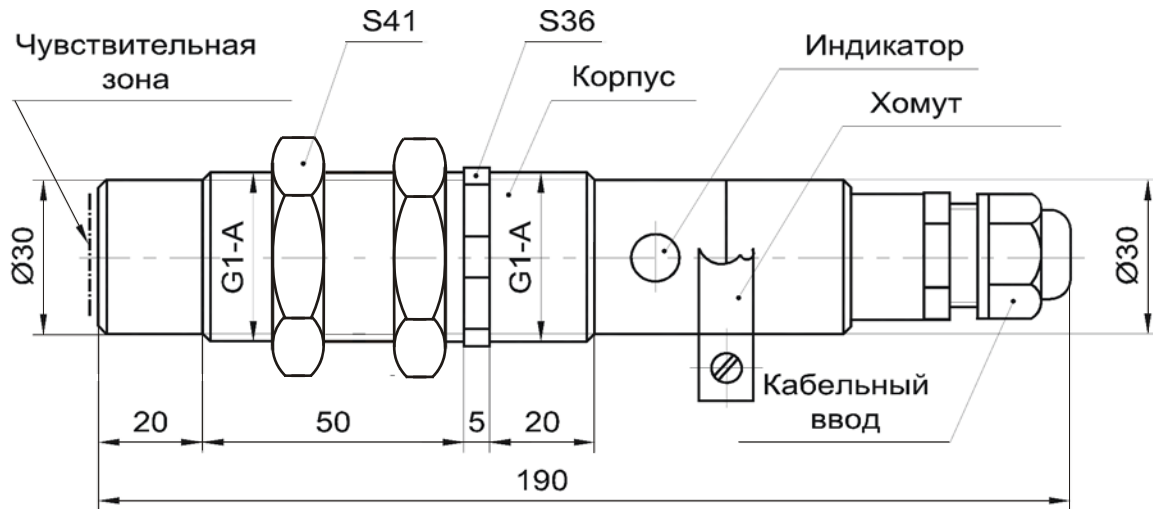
Внешний вид и габаритные размеры датчика
